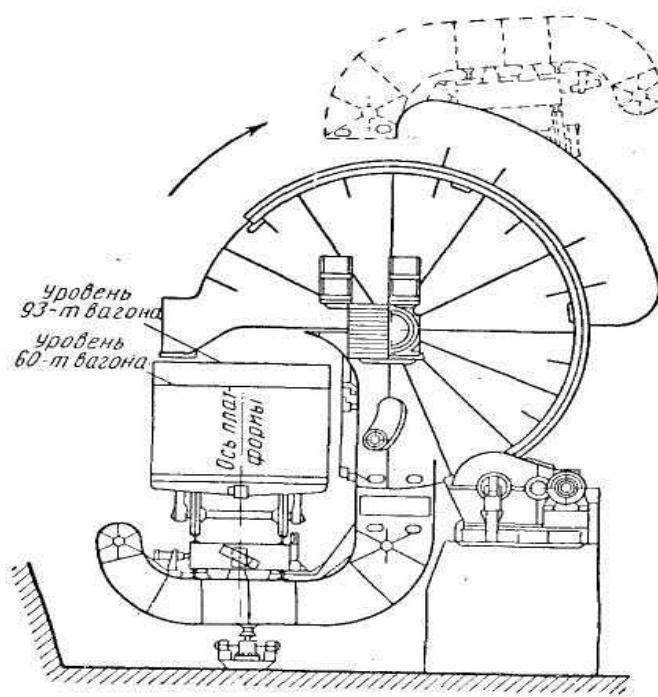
Боковой стационарный вагонопрокидыватель
